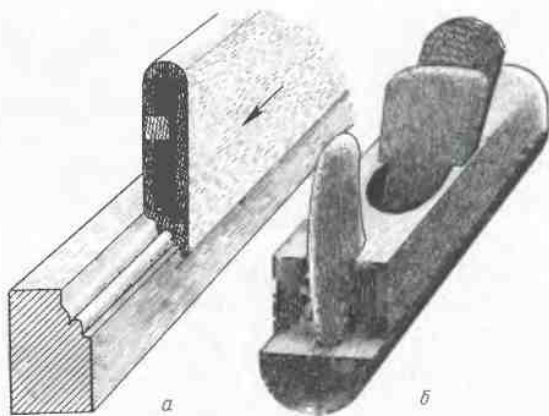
Инструмент для выборки криволинейного профиля: а — калевка; б — галтель со сменными подошвой и железкой
